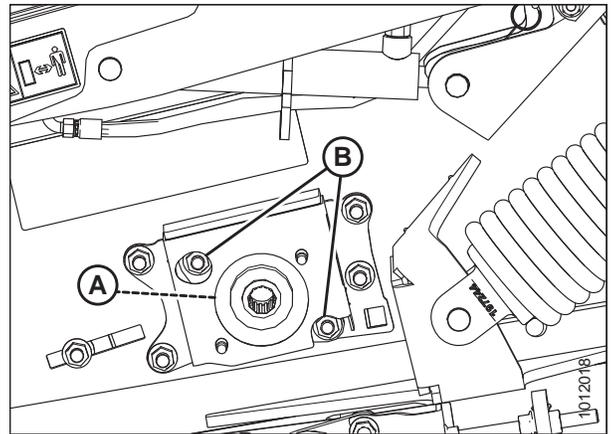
Rodillo de mando de la cama frontal del lado izquierdo
